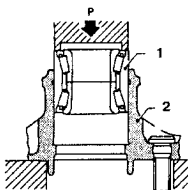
Установка подшипника в ступицу (См. Раздел 7)
